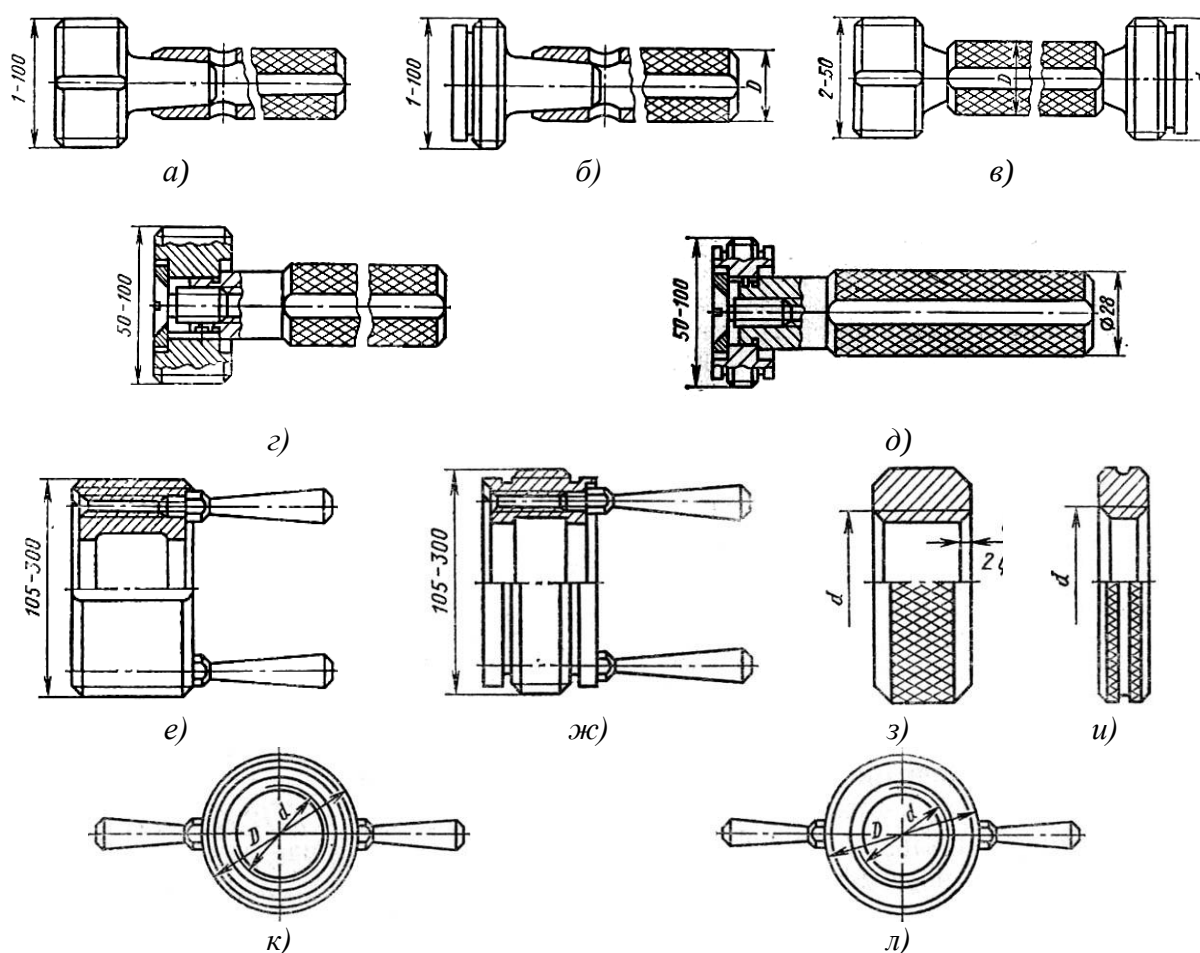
Конструкция резьбовых калибров-пробок и калибров колец:
